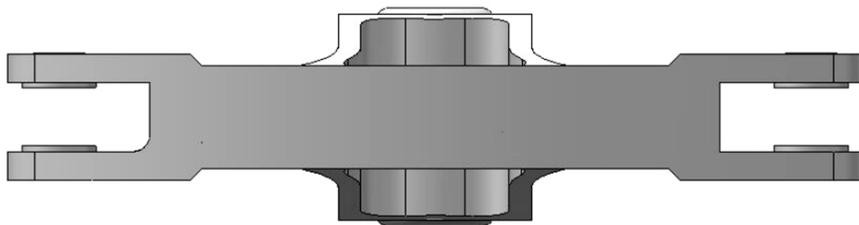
Сборочная единица “Поводок” (вид сверху)
